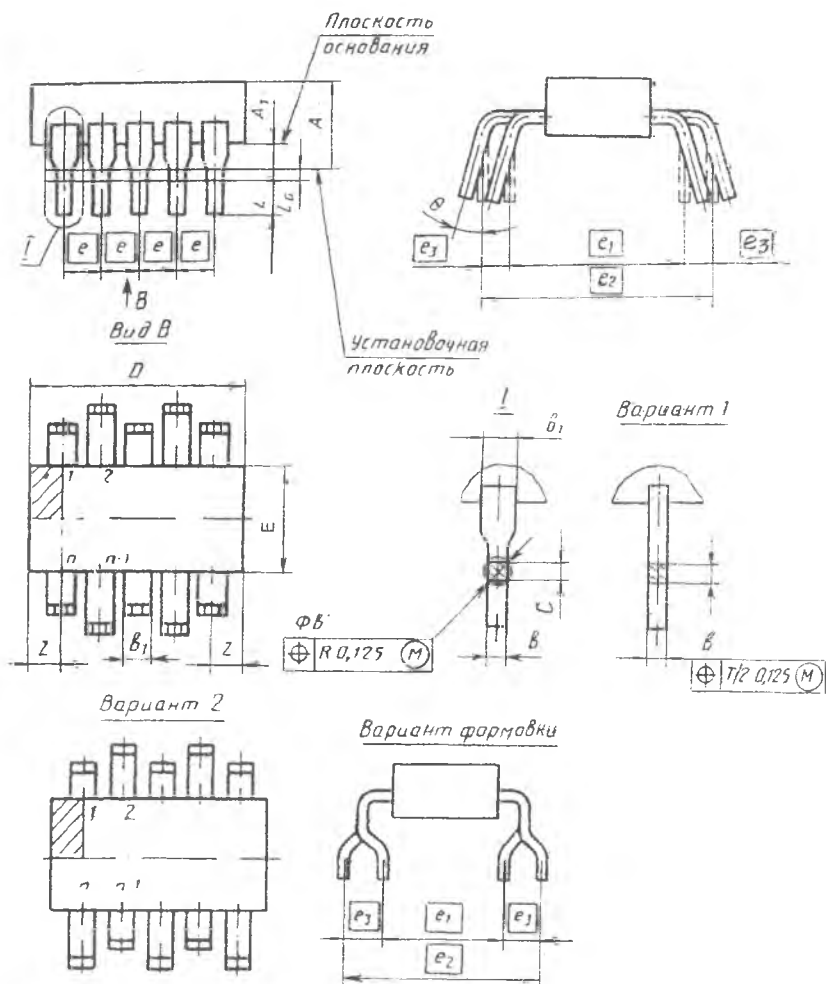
Конструкция корпуса типа 2 подтипа 1
